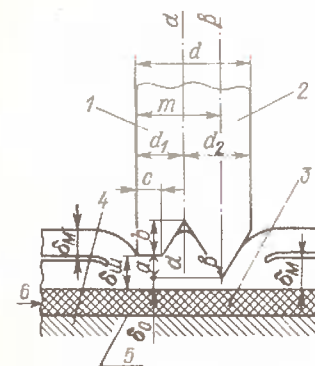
Электрод для сварки фигурного шва с обрезкой:
